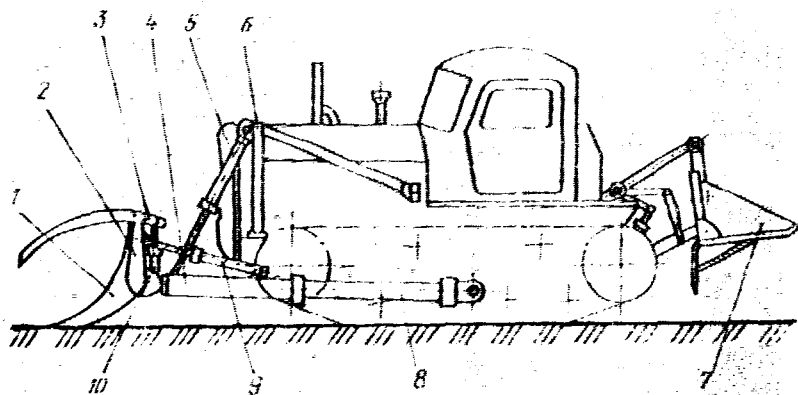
Корчеватель КРТ-75 (конструкция ШИИМЭСХ):
